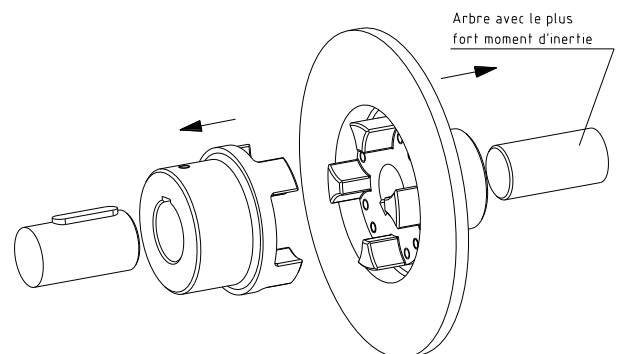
Montage moyeu et moyeu FN avec tambour/disque
